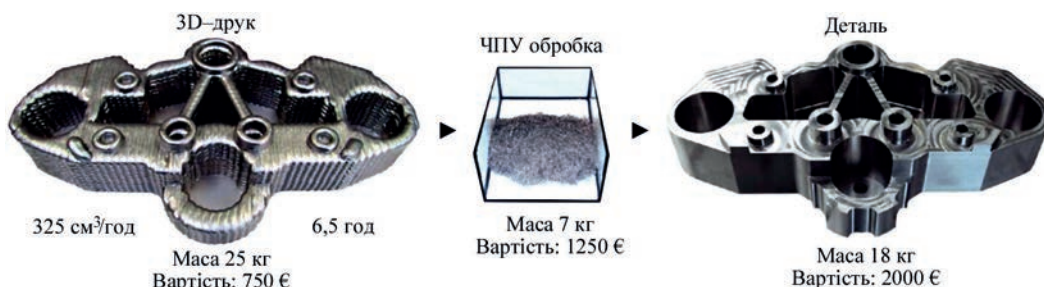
Процес виготовлення металевої деталі адитивним наплавленням [10]
